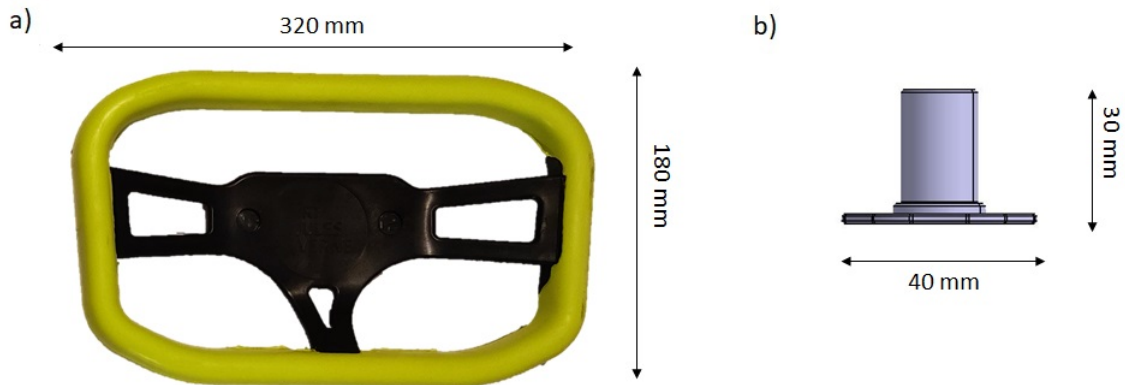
a) Dimensions du volant b) Dimensions de l'insert métallique
